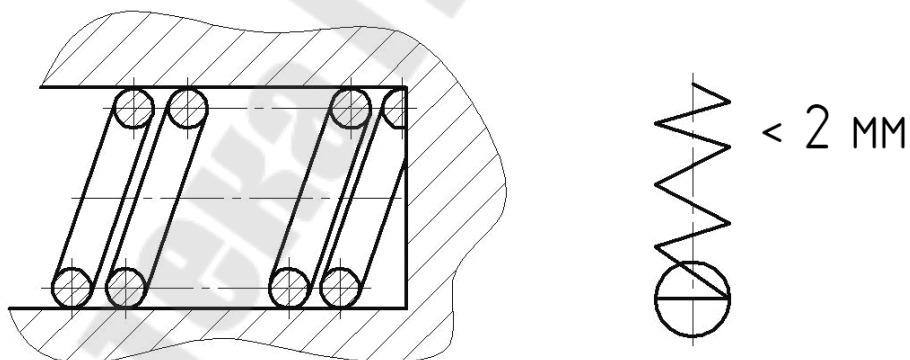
Изображение пружин на чертежах общего вида и сборочном чертеже
